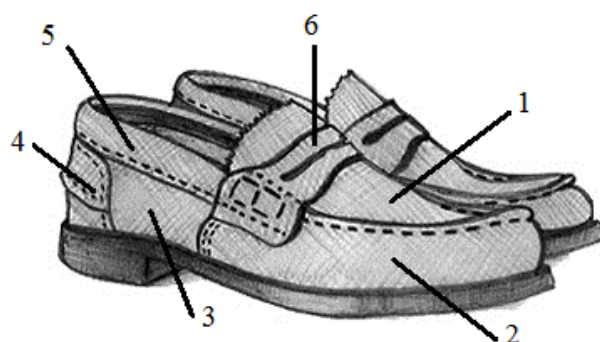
Наружные детали пространственной заготовки полубо-
